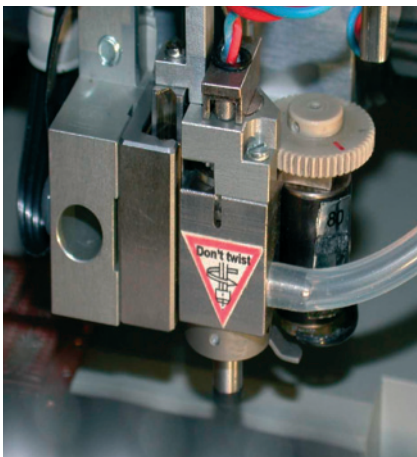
Kernstück der Die-Attach-Maschine ist das »Rotary Bond Tool« mit Mikrogetriebe
